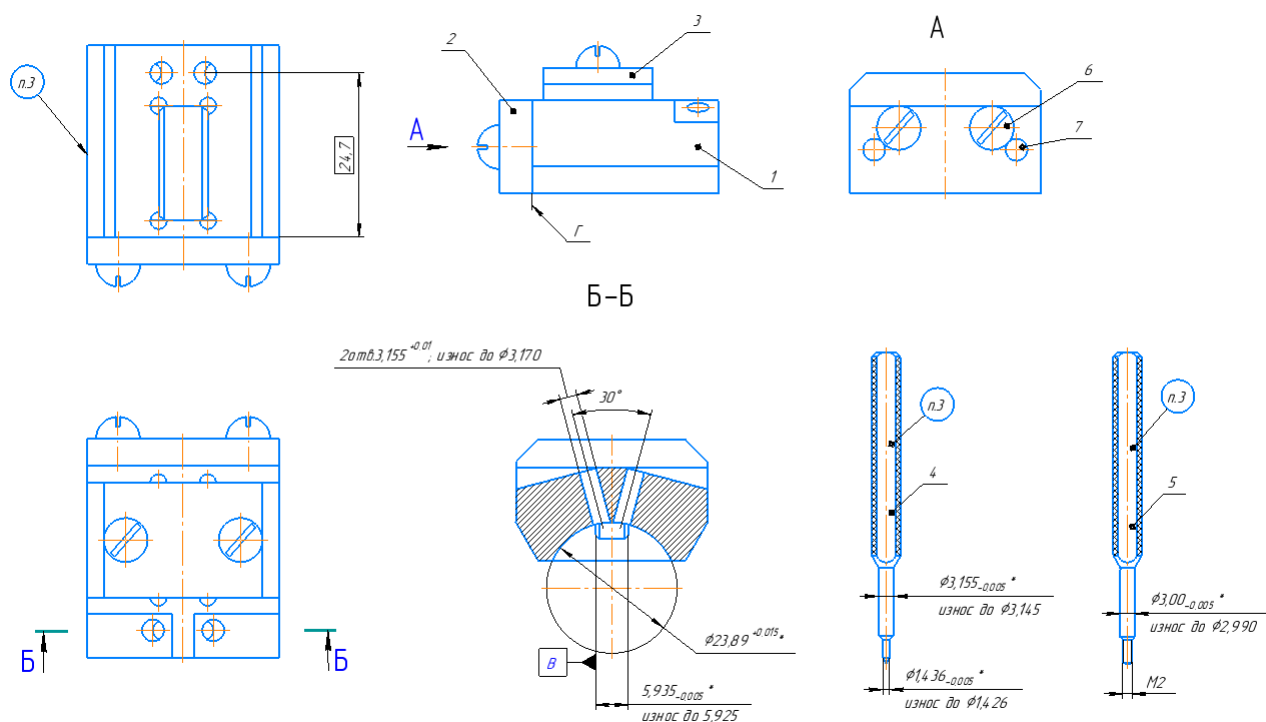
Приспособление для контроля допуска расположения
